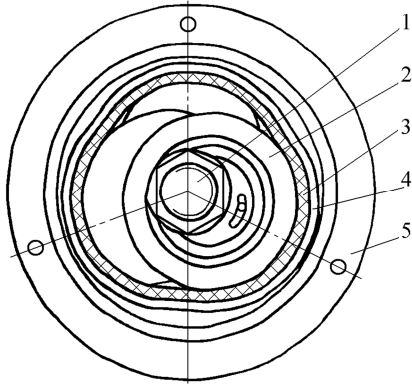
Загальний вигляд трихвильової зубчастої передачі з металополімерним гнучким колесом:
